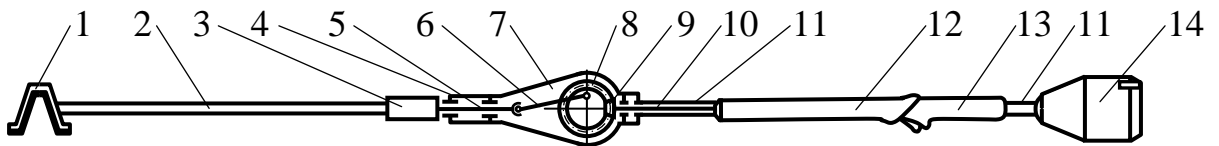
Схема ручного струшувача плодів (патент ЕР 0933015 А1): 1 – захват; 2 – штанга; 3 – з'єднувальна муфта; 4 – корпус збурювача коливань; 5 – повзун; 6 – шатун; 7 – кривошипно-повзунний механізм; 8, 9 – ведена і ведуча конічні шестерні; 10 – вал; 11 – опорна труба; 12 – демпфер; 13 – ручка; 14 – електродвигун
